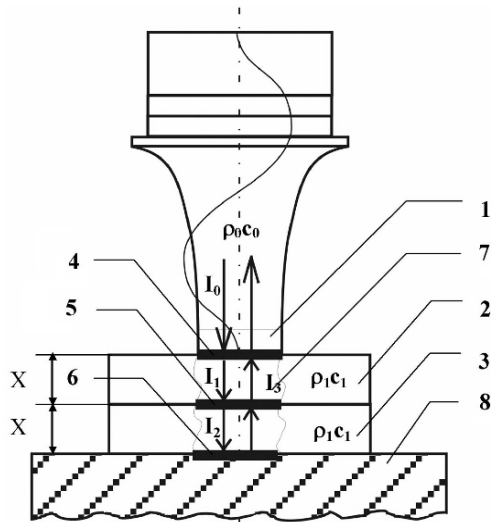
Схема введения ультразвуковых колебаний в свариваемые материалы. 1 – сварочный инструмент; 2, 3 – свариваемые материалы; 4, 5, 6 – границы раздела материалов, инструмента и опоры; 7 – зона сварки; 8 – опора; I_{0-3} – интенсивности ультразвуковых колебаний
